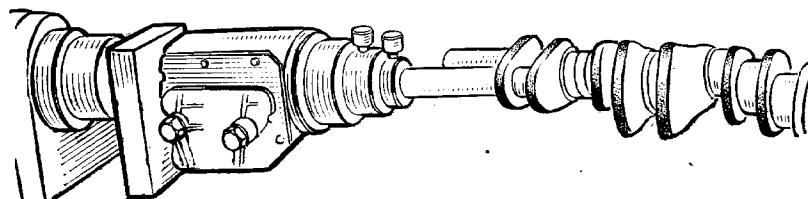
Общий вид стенда для вывертывания пробок коленчатого вала
